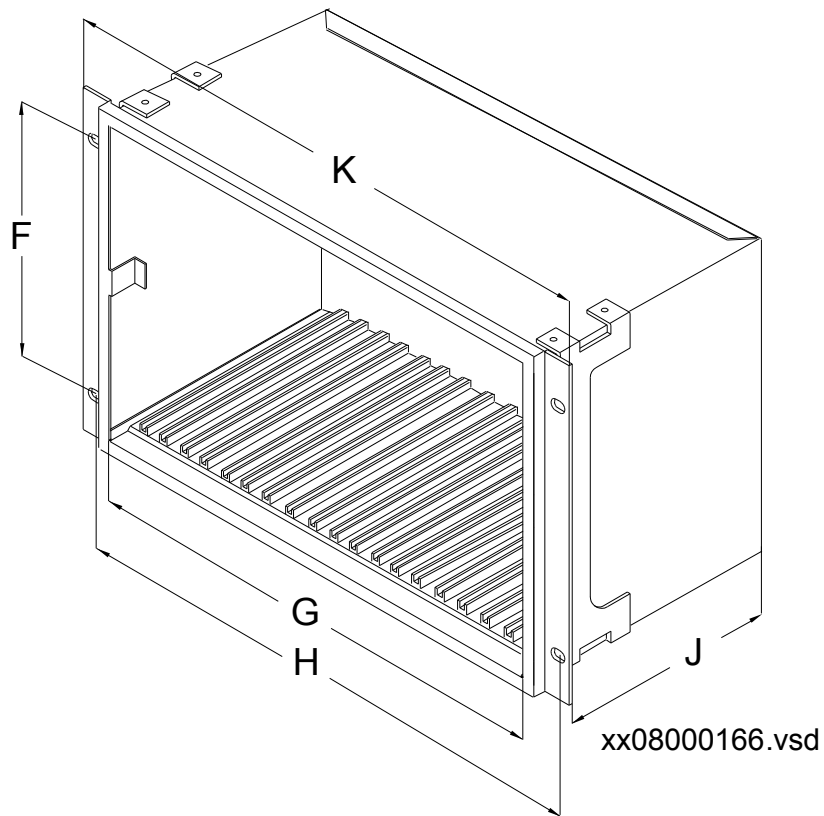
Корпус без задней крышки с комплектом для монтажа в 19-дюймовой стойке
